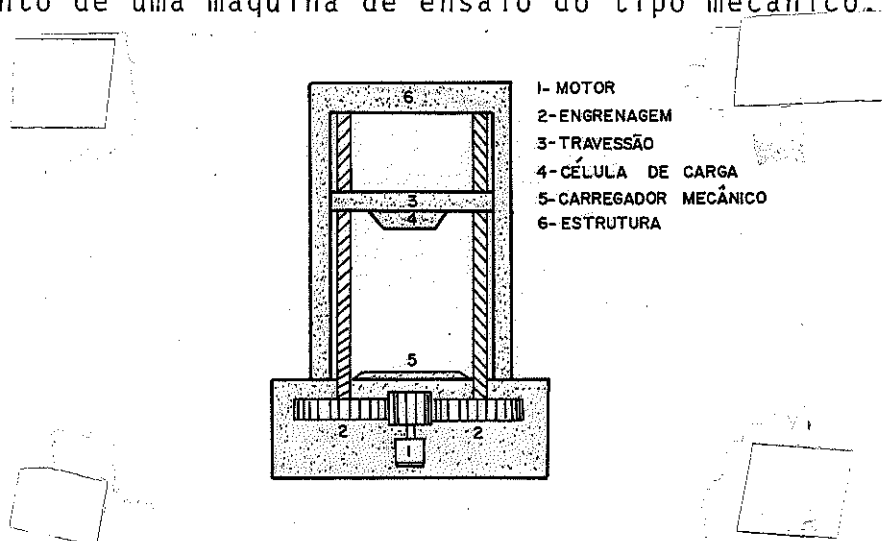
Máquina Universal de Ensaio do Tipo Mecânico
